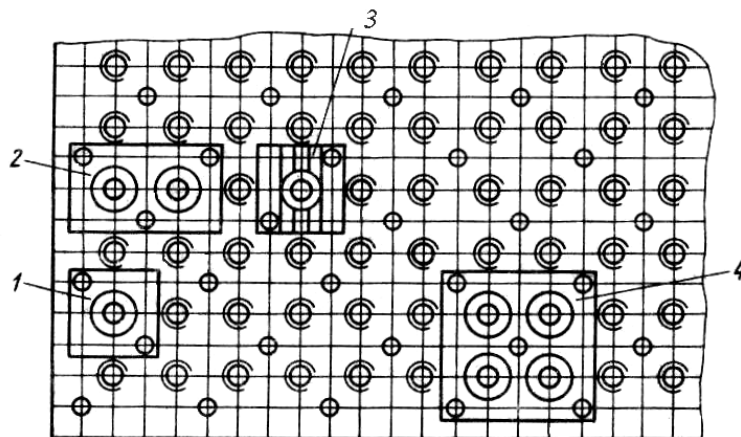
Схема построения типоразмерного ряда корпусных элементов УСПО:
